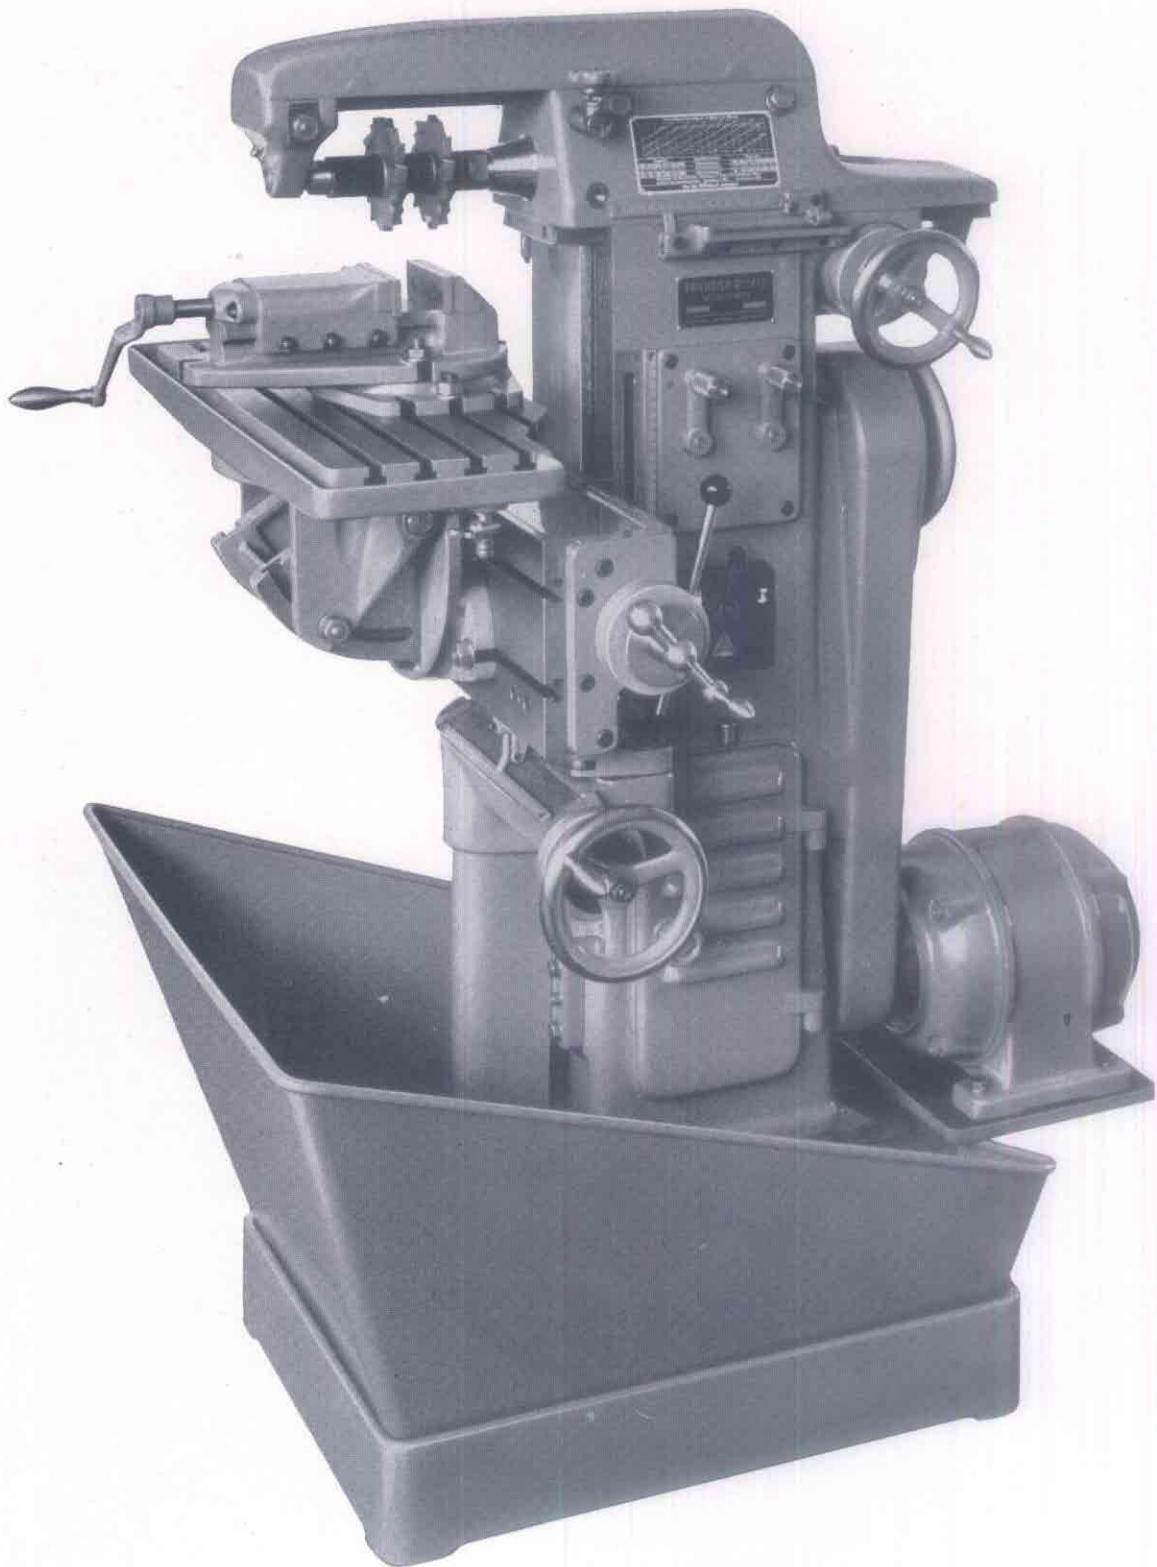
FP1 Maschine mit Gegenhalter, schwenkbarem Winkeltisch mit Schraubstock
